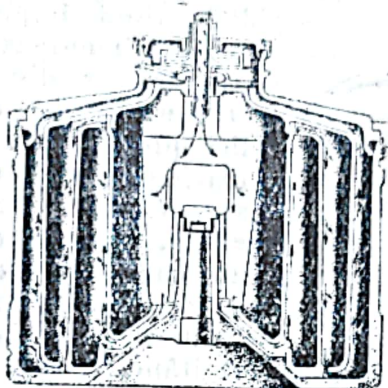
Tamburul cu efect multiplu pentru o centrifugă separatoare.
